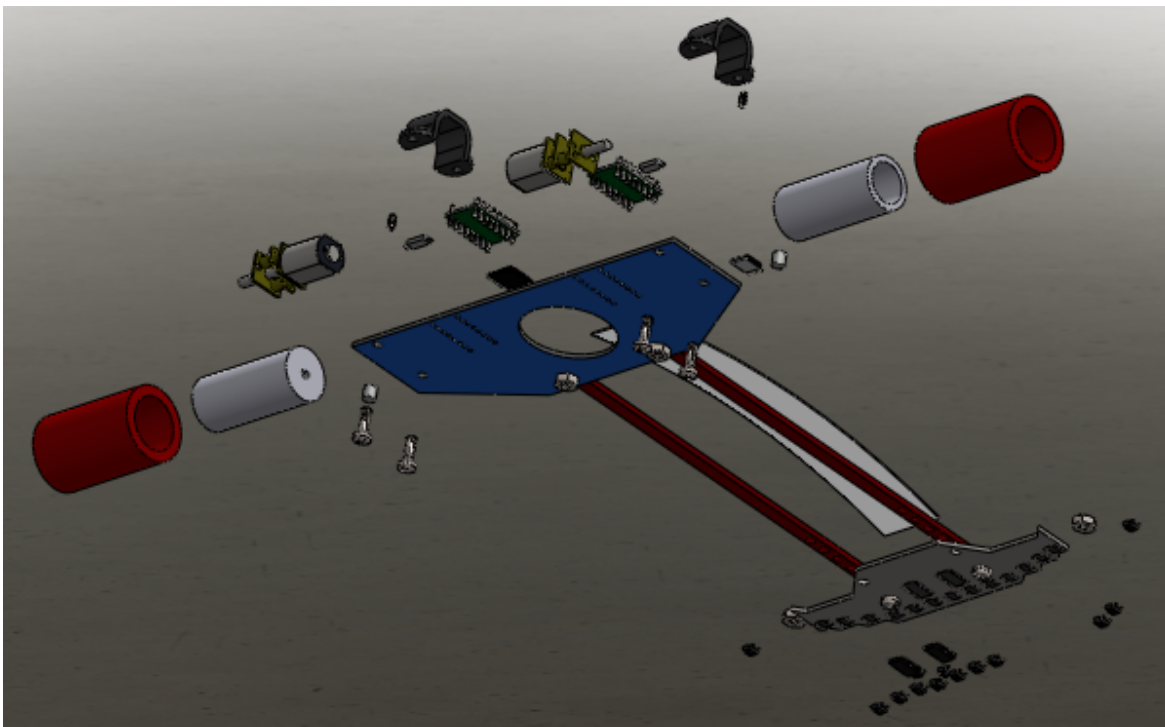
Se muestra el ensamble de cada uno de los componentes del prototipo seguidor de línea.
